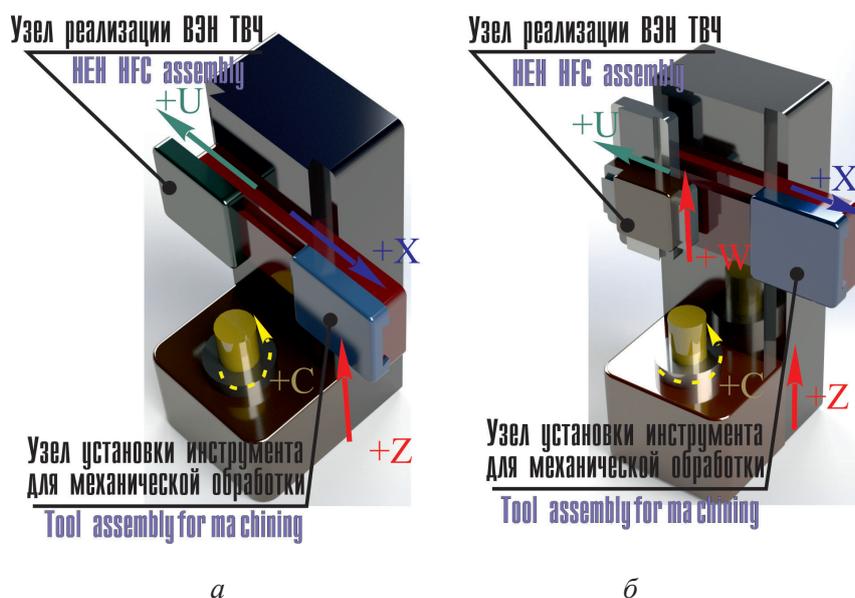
Компонка гибридной металлообрабатывающей системы с вертикальным расположением станины:
